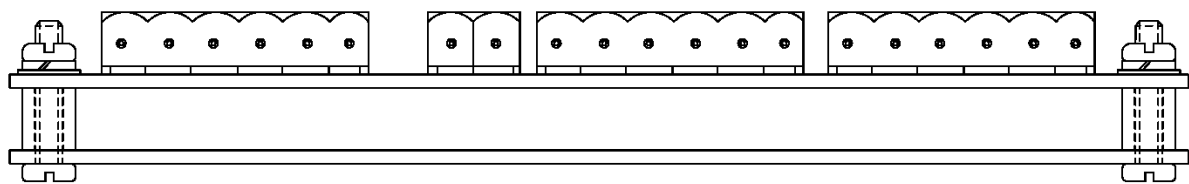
Внешний вид и габаритные размеры КРАБ-2.
